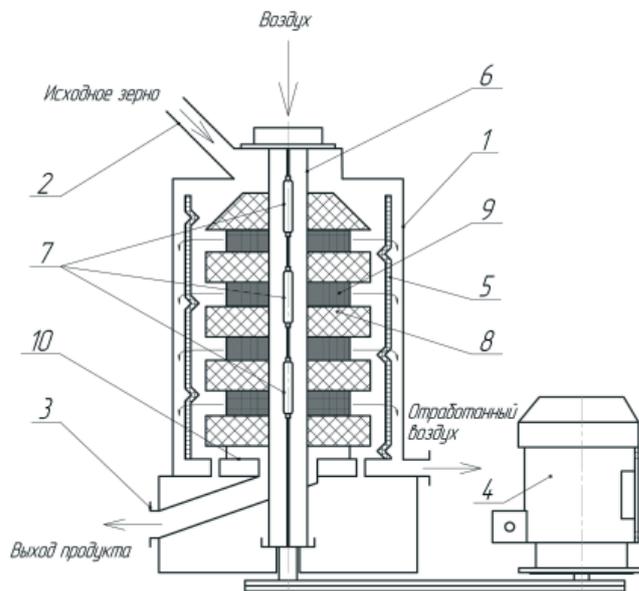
Шелушильно-сушильная установка: 1 – корпус; 2 – загрузочный патрубок; 3 – выпускной патрубок; 4 – электродвигатель; 5 – ситовый цилиндр; 6 – полевой вал с отверстиями; 7 – ИК-излучатели; 8 – абразивные круги; 9 – ситовые обечайки; 10 – вентилятор
